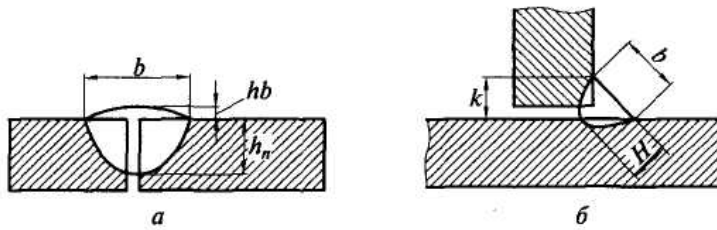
Геометрическое очертание сечения сварных швов:
